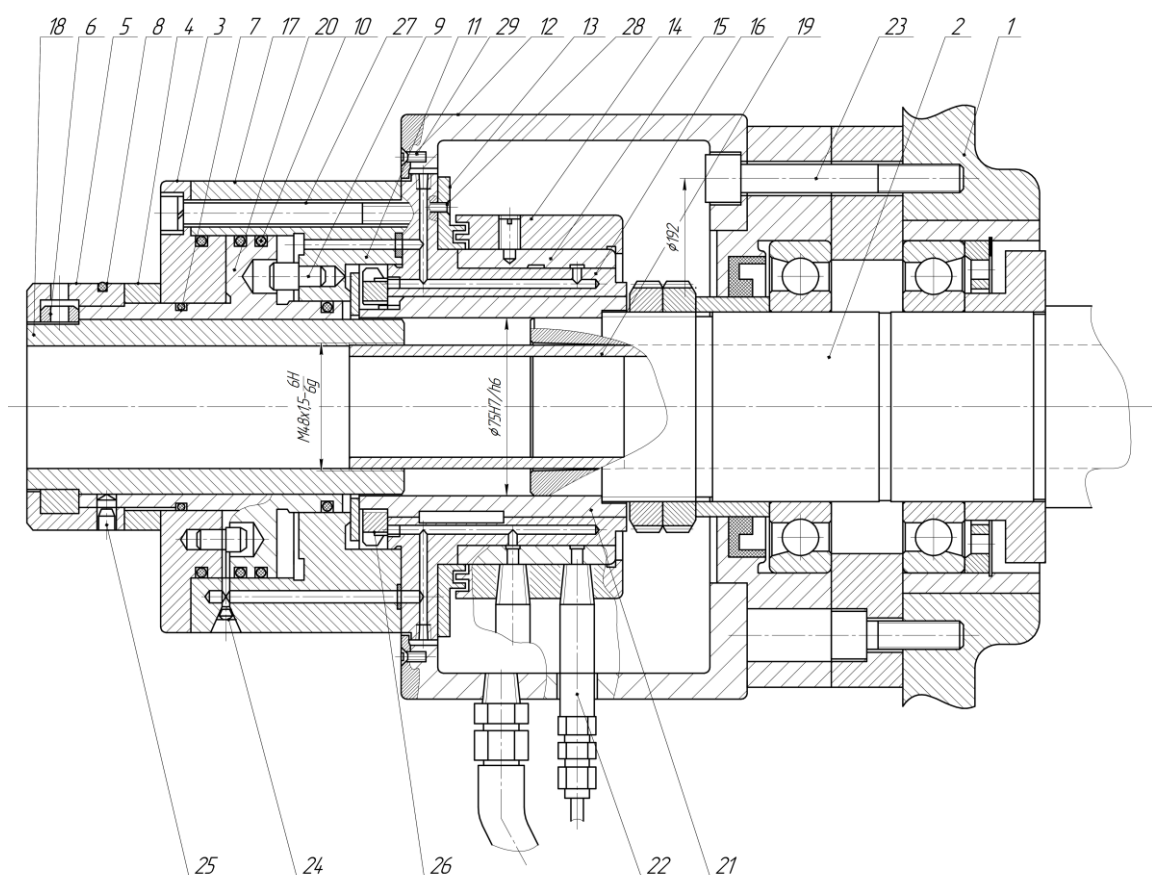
Обертовий гідравлічний циліндр з нерухою маслопідвідною втулкою токарного верстату з ЧПК
